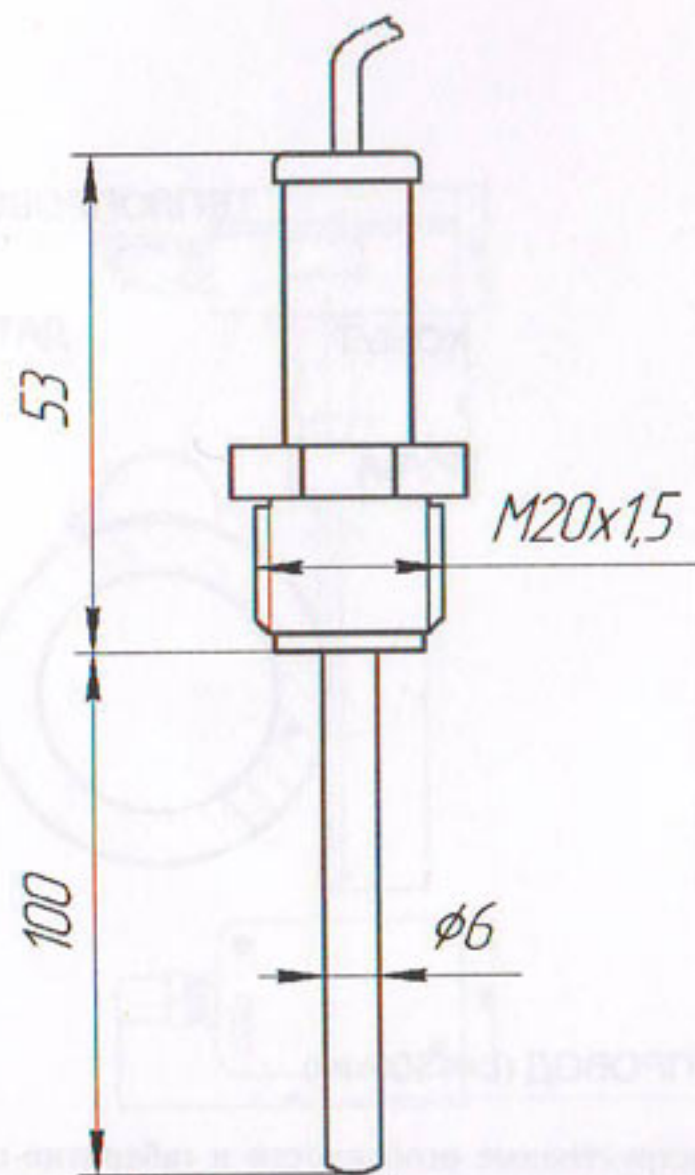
Конструктивные особенности и габаритно-присоединительные размеры датчика СТВ-04
